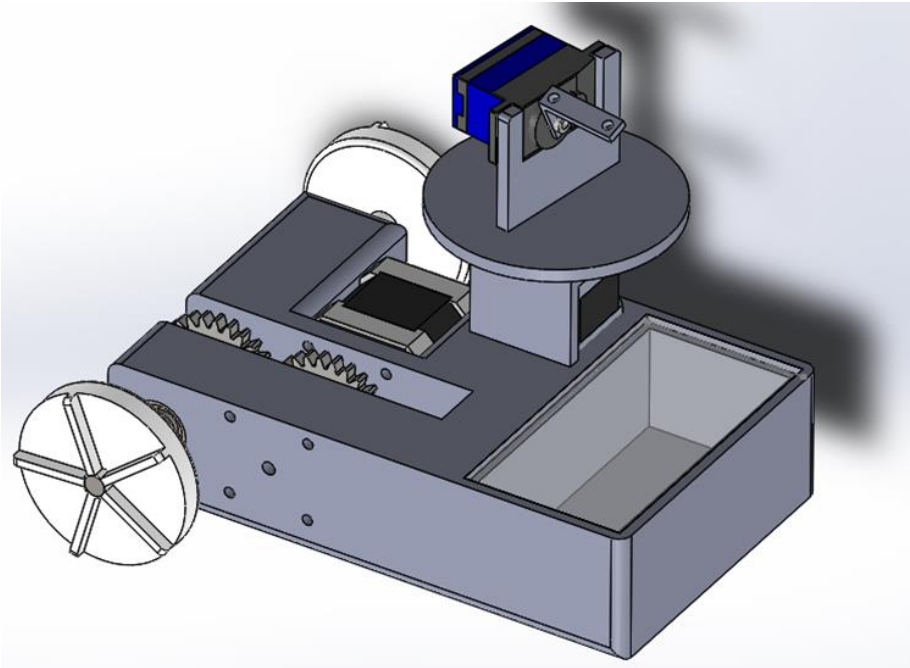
Equipo con transmisión por engranajes [el autor]
